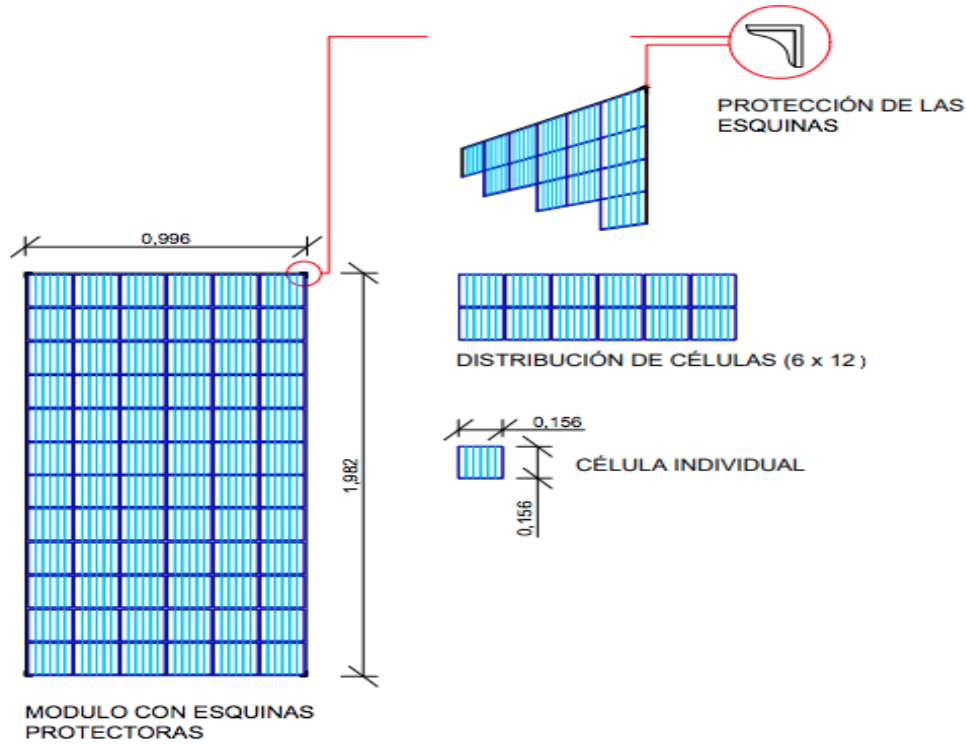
Vista del panel solar seleccionado en perfil vertical y horizontal (las medidas están dadas en metros).
